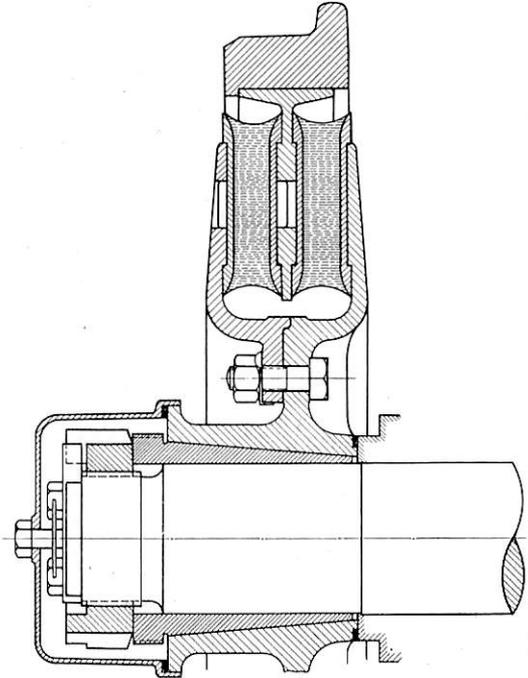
Gummigefederter Radsatz mit aufgeschraubten Rädern.
